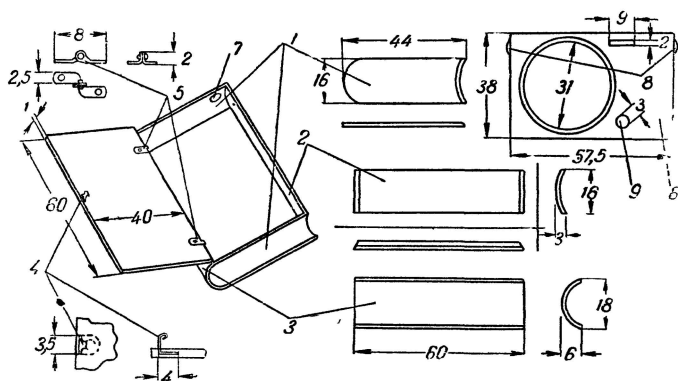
Корпус приемника и его детали: 1 — верхняя и нижняя части торца корпуса; 2 — правая часть торца; 3 — левая часть торца (корешок книги); 4 — застёжка; 5 — шарниры; 6 — отражательная доска (заглавный лист); 7 — углубление для крепления детали 6; 8 — выступы для крепления; 9 — отверстие для выключателя.
